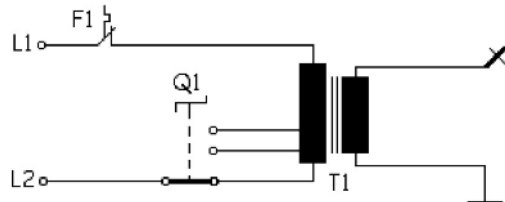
Equipo de soldadura con regulación por conmutador.
